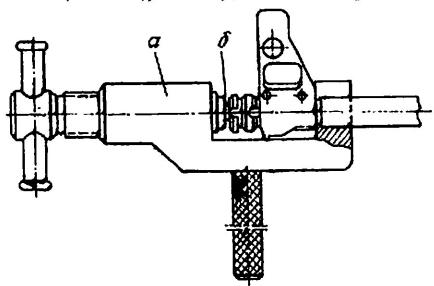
Схема установки струбцины: а — струбцина: 6 — стержень
